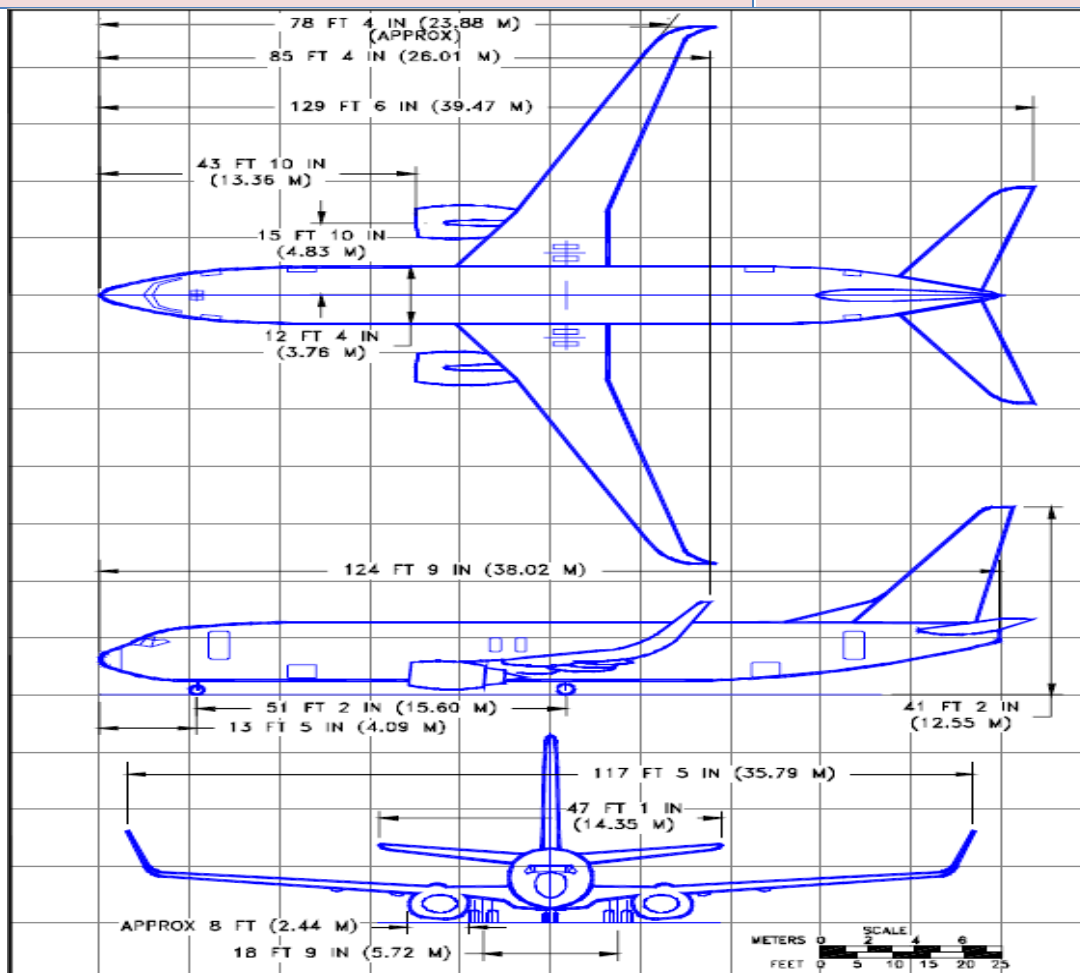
Arrangement générale et les premières dimensions pour une configuration avec Winglets B737-800
